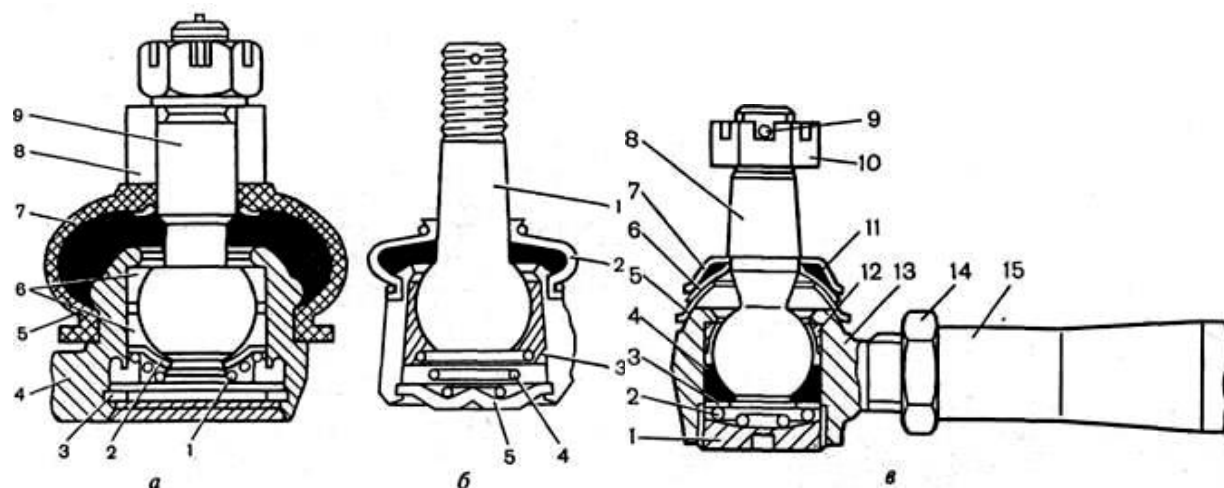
Шарниры рулевых тяг: *а* — автомобиля ИЖ-2715: 1 — пружина; 2 — нажимная обойма; 3 — стопорное кольцо; 4 — рулевая тяга; 5 — пружинное кольцо; 6 — опорный вкладыш; 7 — защитный чехол; 8 — поворотный рычаг; 9 — палец шарнира; *б* — автомобиля ВАЗ-2109: 1 — палец шарового шарнира; 2 — защитный колпачок; 3 — вкладыш шарового пальца; 4 — пружина; 5 — стопорная шайба; *в* — автомобиля УАЗ-31512: 1 — заглушка; 2 — пружина; 3 — пята; 4 — вкладыш; 5 — нижняя сферическая шайба; 6 — верхняя сферическая шайба; 7 — пружинный колпачок; 8 — палец; 9 — шплинт; 10 — гайка; 11 — защитное кольцо; 12 — сухарь; 13 — наконечник; 14 — гайка; 15 — рулевая тяга.
